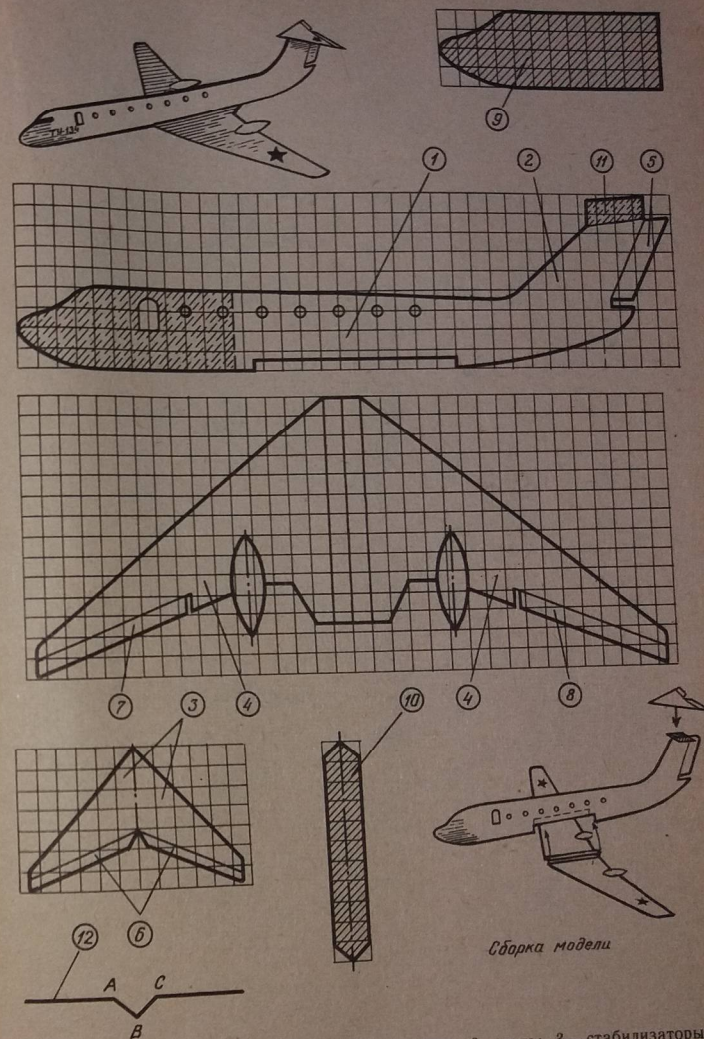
Модель самолета Ту-134: 1— фюзеляж; 2— киль; 3— стабилизаторы; 4— крылья; 5— руль поворота; 6— руль высоты; 7— элерон левый; 8— элерон правый; 9— груз из картона; 10— дополнительная деталь; 11— клапан для клея; 12— схема изгиба крыльев
